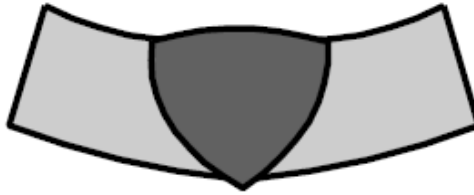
Esquema de deflexión de una junta soldada [8].
